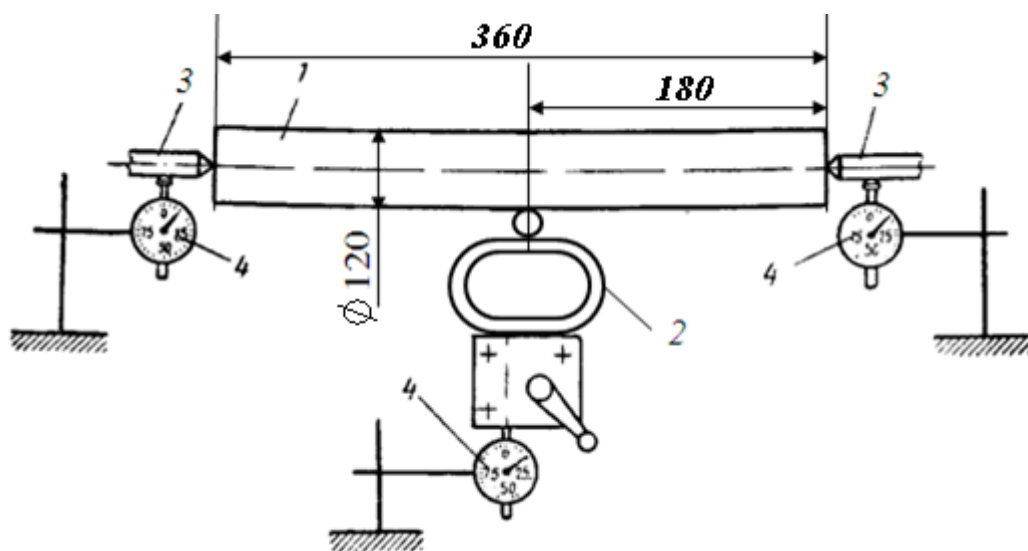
Схема экспериментальной установки для измерения жесткости токарного станка: 1 – заготовка; 2 – динамометр; 3 – центры; 4 – индикаторы.
